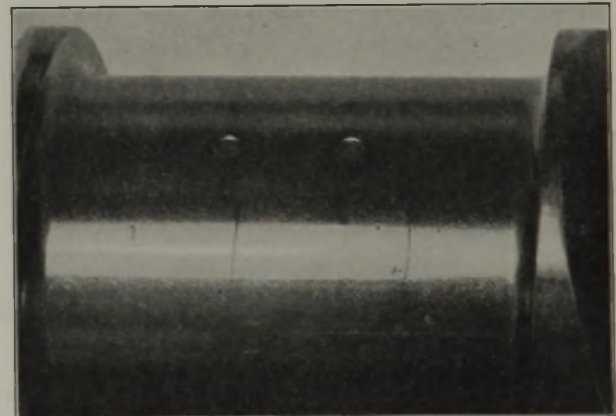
Durch Magnetstoß magnetisiert, anschließend mit Metallöl bespült.
